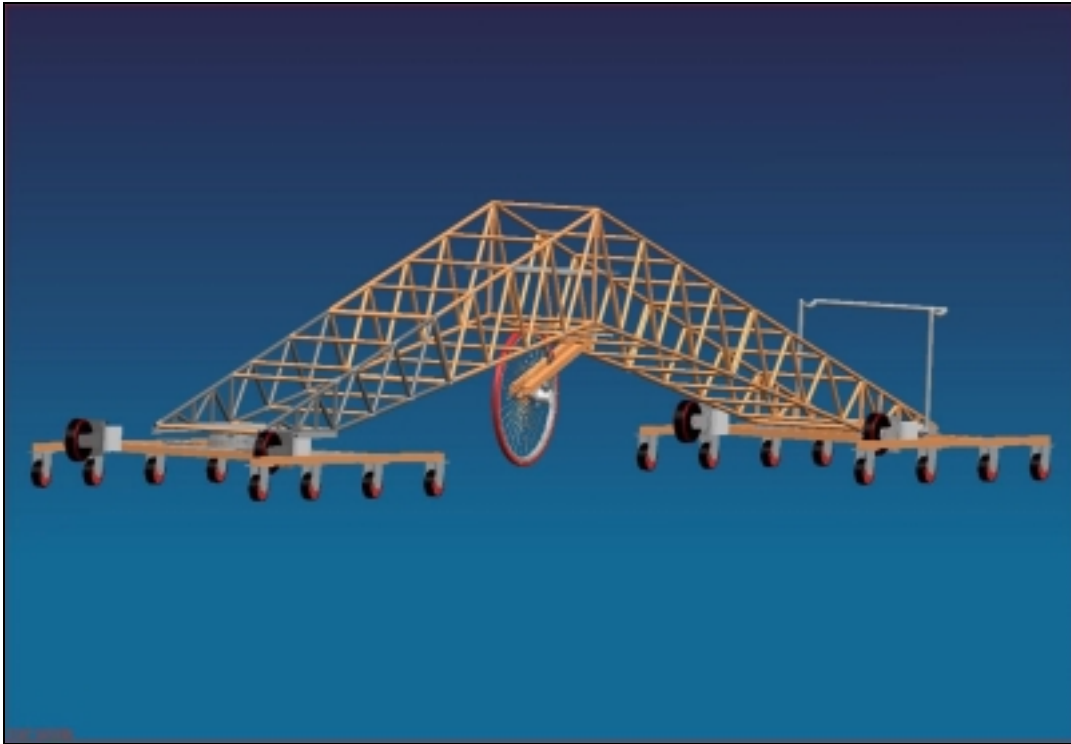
Estructura del perfilógrafo del Instituto de Ingeniería UNAM.
